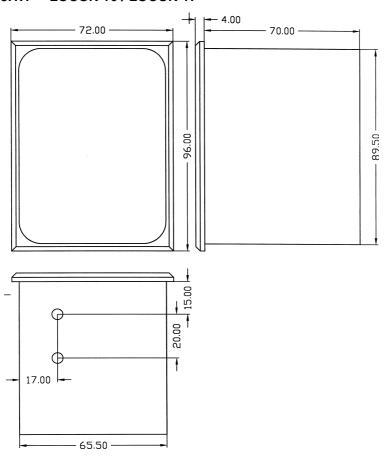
plan coté technique LOCON 16 / LOCON 17
